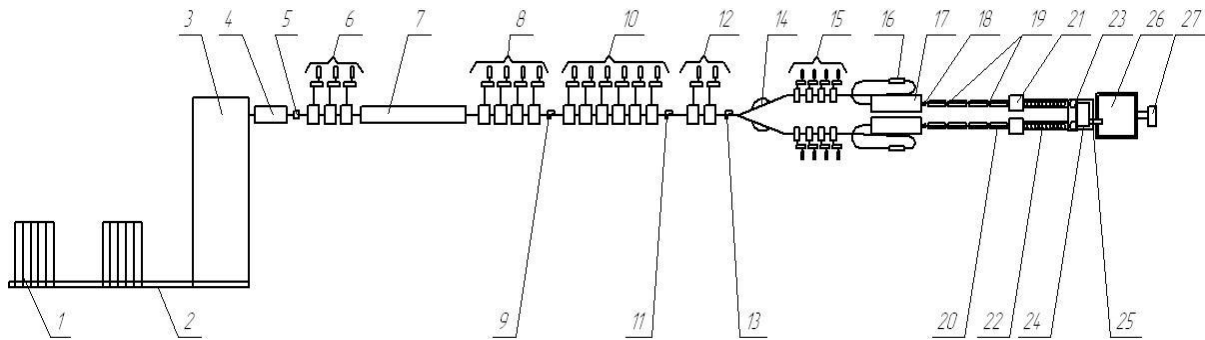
Схема расположения оборудования стана 170: 1 – загрузочные столы; 2 – рольганг с платформой для взвешивания; 3 – нагревательная печь; 4 – рольганг для аварийного сброса заготовок; 5 – установка гидросбива окалины; 6 – обжимная группа клеток; 7 – промежуточный сдвоенный рольганг с теплоудерживающими крышками; 8 – черновая группа; 9, 11, 13 – летучие ножницы; 10, 12 – первая и вторая промежуточные группы; 14 – горизонтальный петлеобразователь; 15 – предчистовые группы с вертикальными петлеобразователями; 16 – промежуточная секция водяного охлаждения; 17 – десятиклетьевые чистовые блоки; 18 – установка контроля размеров проката; 19 – трайб-аппараты; 20 – линия водяного охлаждения; 21 – виткообразователь; 22 – конвейер воздушного охлаждения; 23 – виткосборник; 24 – транспортер с палетами; 25 – кантователь; 26 – участок отделки бунтов; 27 – тележка накопления бунтов
